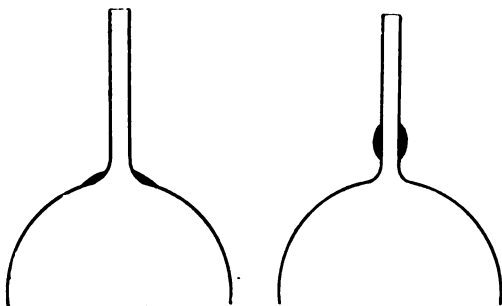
Vue schématique du tube de verre soudé à l'ampoule avant et après son étirage.
